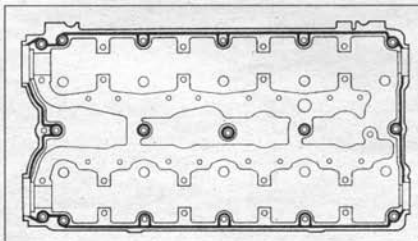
Схема нанесения герметика на верхнюю плоскость головки цилиндров
